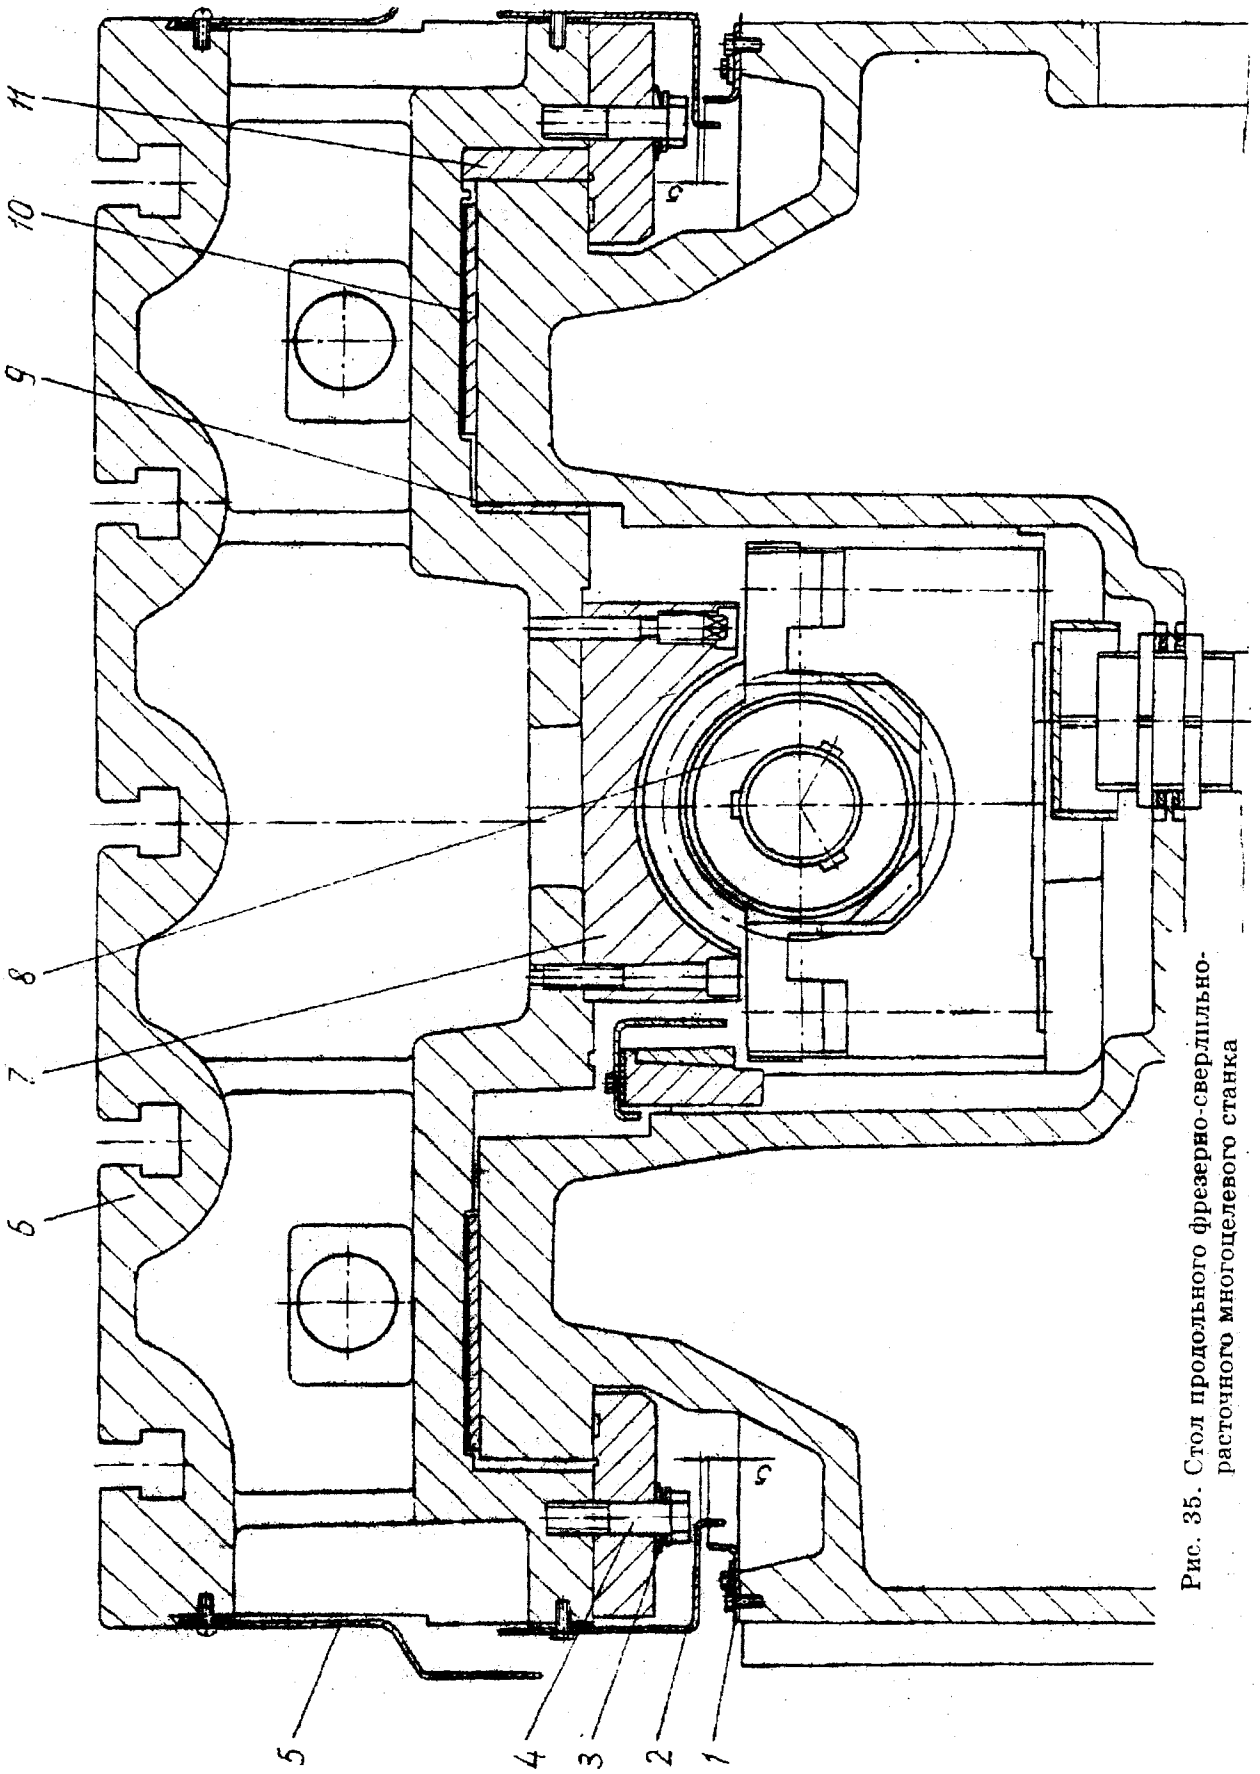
Стол продольного фрезерно-сверильно-расточного многоцелевого станка
